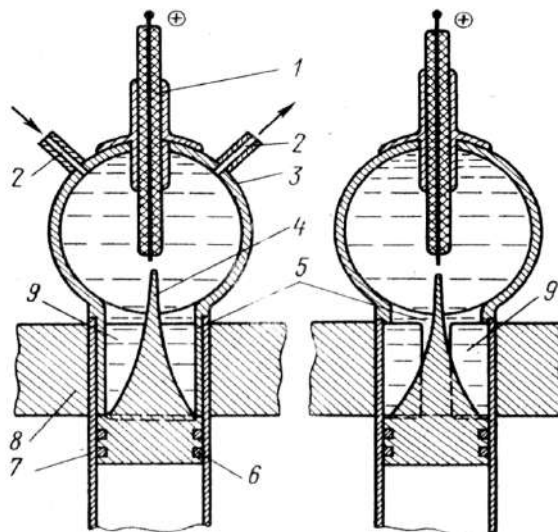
Схема пристрій для електрогідравлічного розвальцьовування трубок жорстким патроном: 1 - позитивний електрод; 2 - патрубки для підведення і відведення води; 3 - корпус пристрою; 4 - негативний електрод (виступ корпусу); 5 - сполучна перемичка корпусу; 6 - сальники; 7 - вальцьована трубка; 8 - трубна дошка; 9 - вікна корпусу
